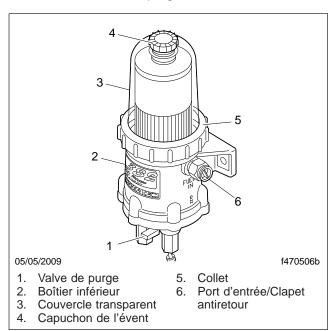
, Séparateur carburant/eau DAVCO (modèle Fuel Pro 382 illustré)
